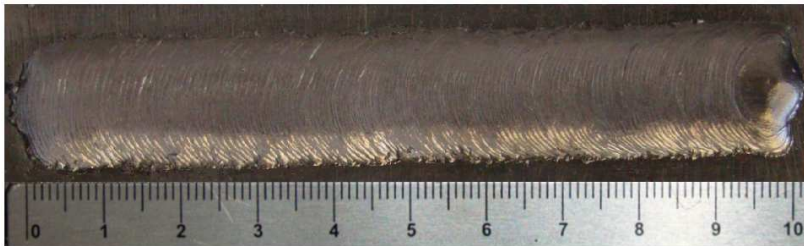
Cordão de solda realizado com alta velocidade de tecimento
